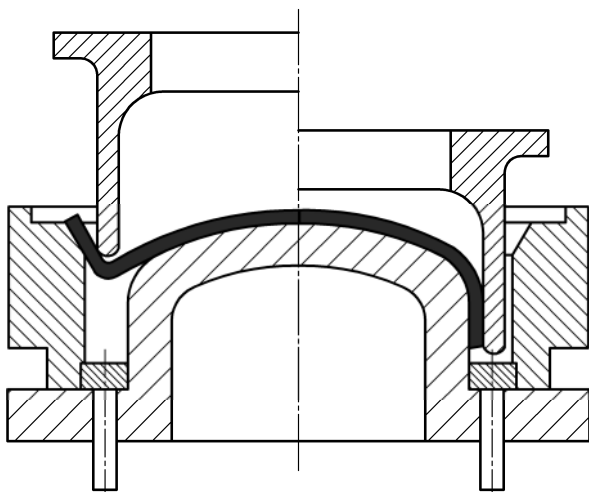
Штамп для витягування реверсивним способом напівсферичного днища
